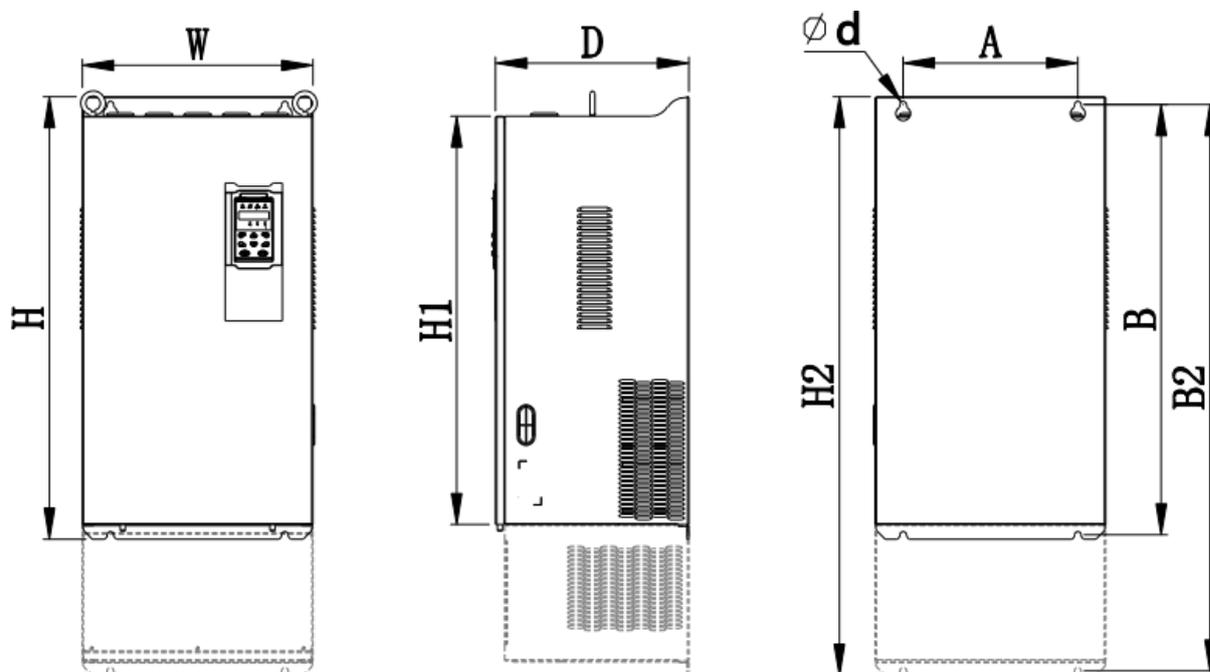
Dimensión TAMAÑO H ~ J (110KW-250KW)
